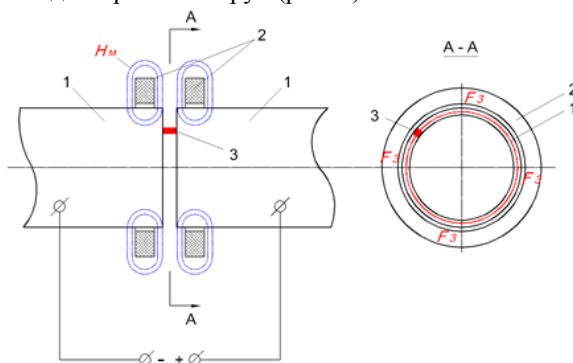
Схема зварювання дугою що обертається в магнітному полі
